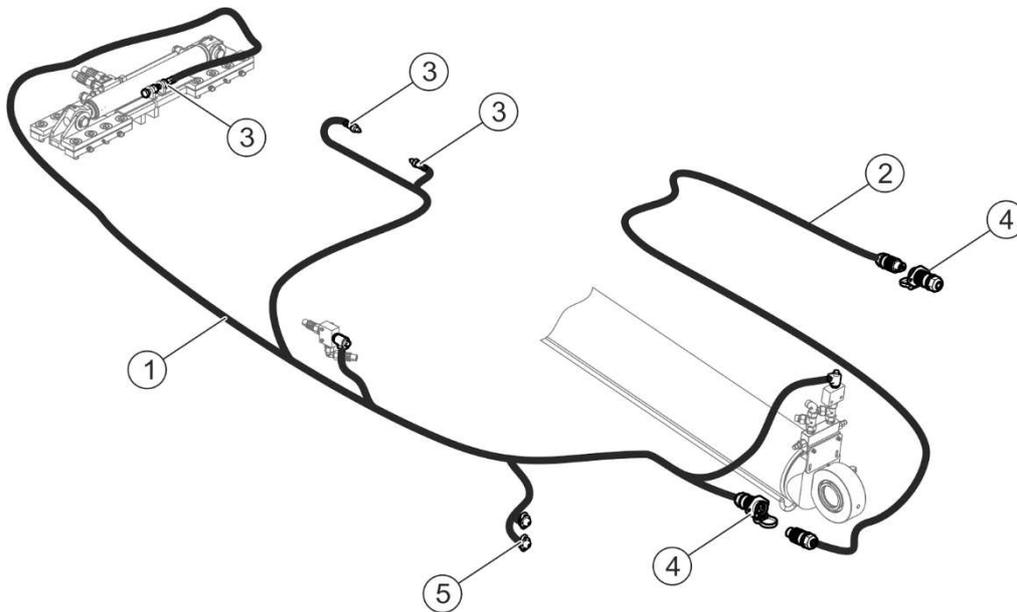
Aufbau der Elektroinstallation der Hydraulikanlage
